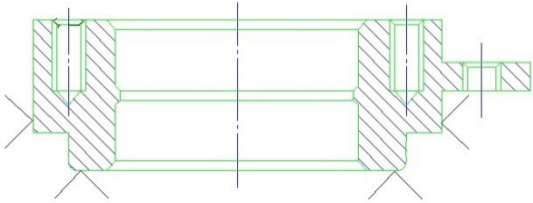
Заготовка деталі стакан Р6-ВС. 07-00-05”
